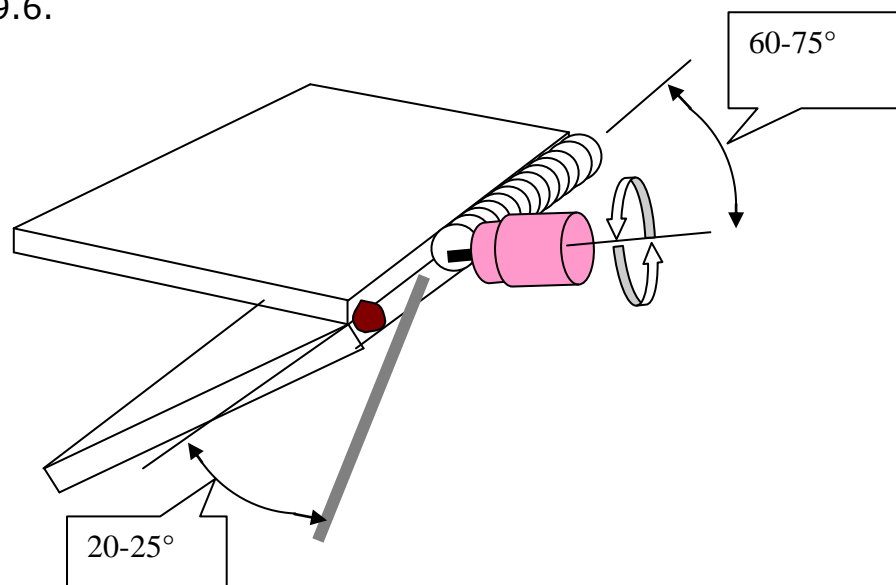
Realización de soldadura de costura de filete de junta en esquina en posición horizontal sobre placa.
